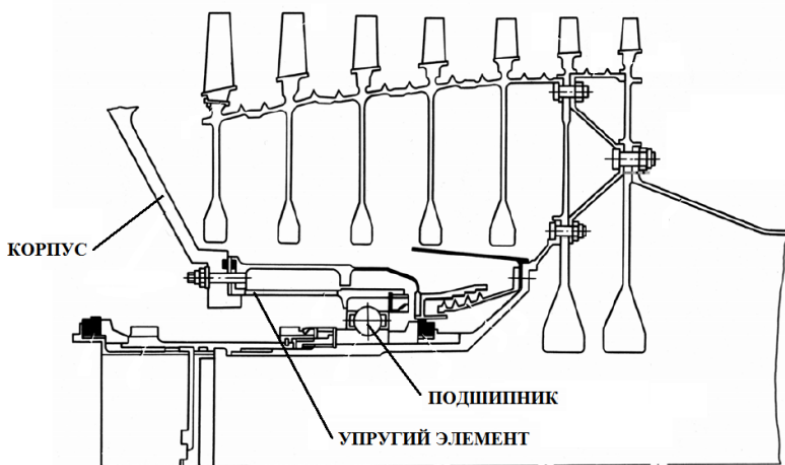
Схема опоры ротора компрессора высокого давления двигателя Д-36
